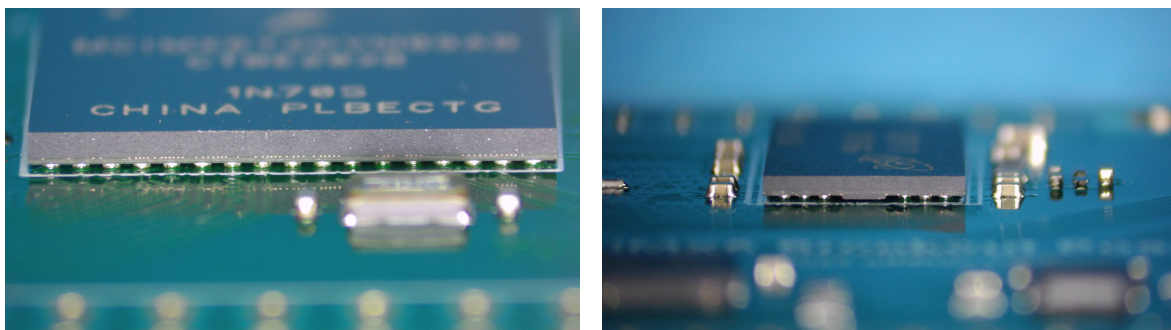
Detalle de la soldadura de los componentes BGA.
